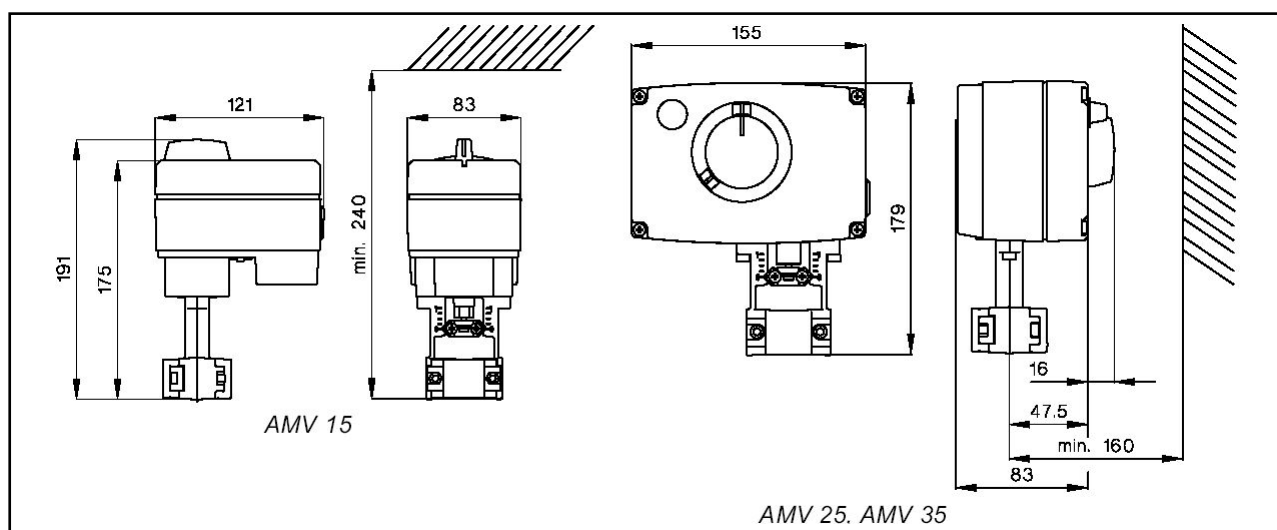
Габаритные и присоединительные размеры AMV 15, 25, 35.
